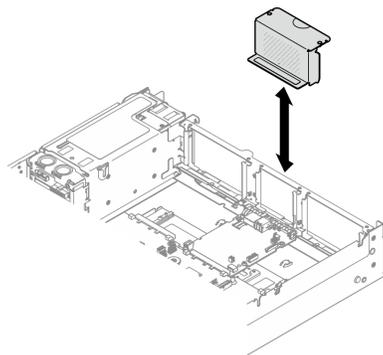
Entfernen der Abdeckblende für Adapterkarte
